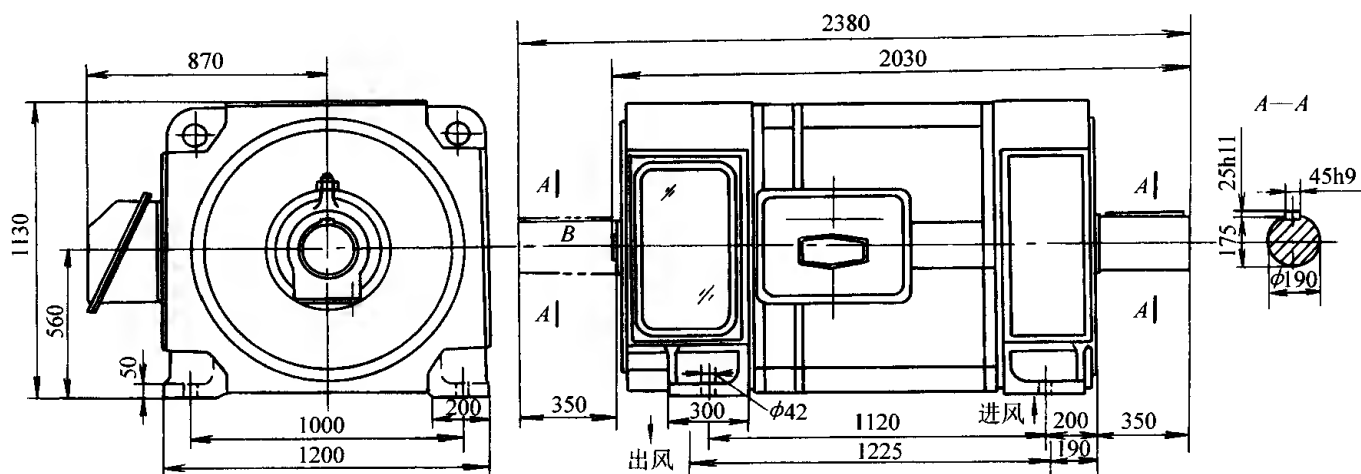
ZD3-560SIP 型 630kW 660V 500/1000r/min IC37 直流电动机安装及外形尺寸图
